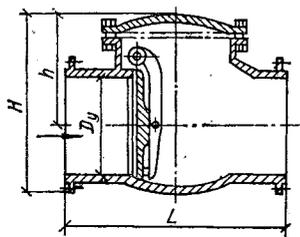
Клапан обратный поворотный чугунный фланцевый.
